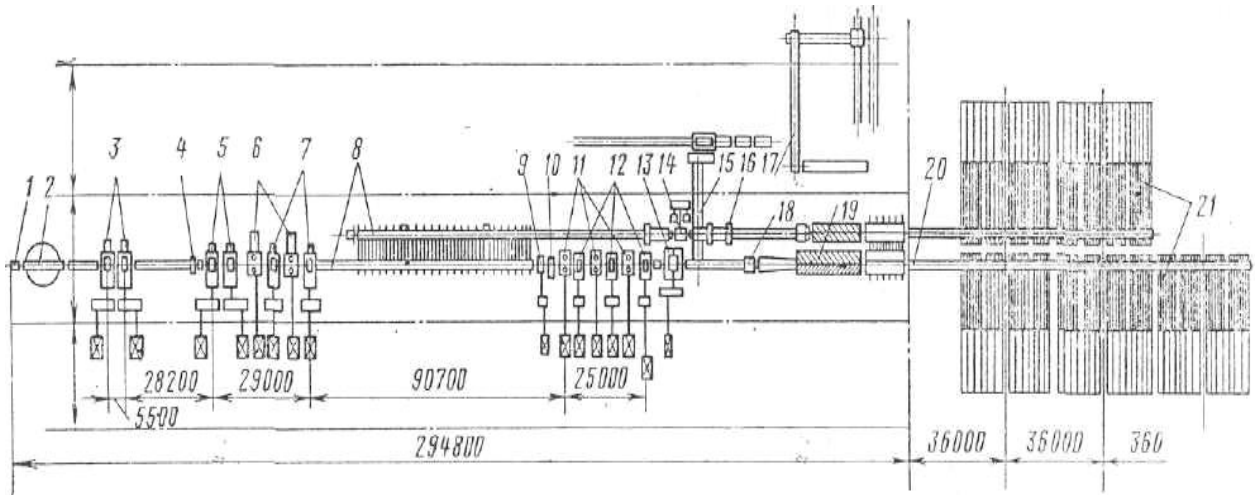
Схема розташування устаткування безперервного заготовочного стану 900/700/500: 1 - рольганг, що підводить, від бльомінга 1300; 2 - поворотний пристрій; 3 - дві кліті дуо 900 мм; 4 - кантувач; 5 - дві кліті дуо 900 мм; 6 - дві вертикальні кліті 700 мм; 7 - дві кліті дуо 700 мм; 8 - рольганги; 9 - маятникові ножиці для відрізки переднього кінця; 10 - кантователь; 11 - три вертикальних кліті 500 мм; 12 - три кліті дуо 500 мм; 13 - летучі планетарні ножиці 150 т; 14 - ножиці з нижнім різом 1000 т; 15 - транспортер для збирання обрізків від ножиців; 16 - пересувний упор за ножицями; 17- колодязь для окалини і транспортуючий пристрій; 18 - клеймована машина; 19-пакетувальні рольганги; 20 - рольганги; 21 - холодильники
